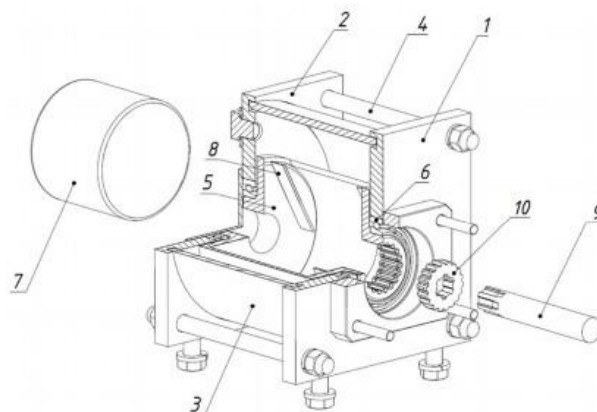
Інерційний віброзбудник планетарного типу: 1 – плита фронтальна; 2 – плита тилова; 3 – труба; 4 – шпилька; 5 – ротор; 6 – підшипник; 7 – бігунки; 8 – напрямна ротора; 9 – вал шліцьовий; 10 – шестірня приводна.
